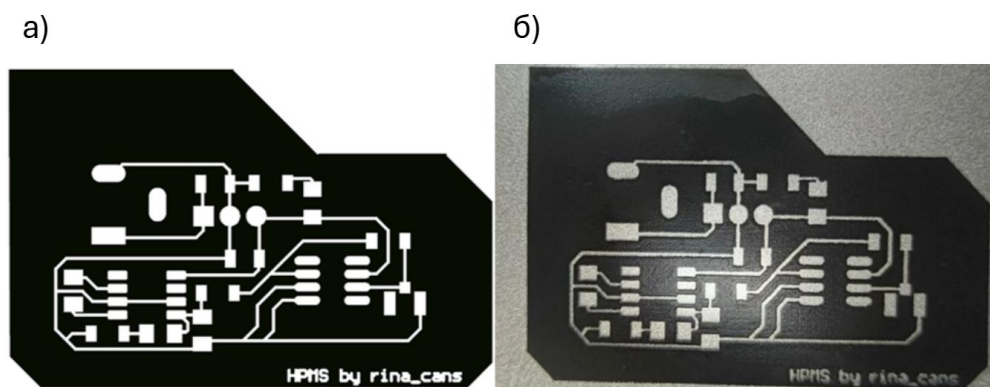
Негативный фотошаблон проводящего рисунка печатной платы:
